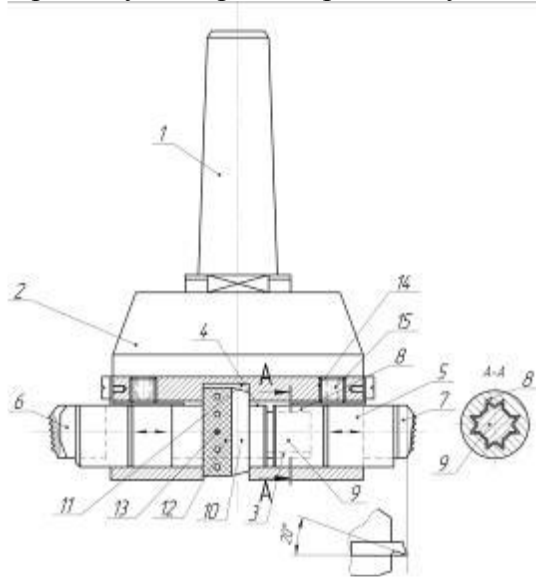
Універсальний пристрій для розточування отворів і нарізання різи
